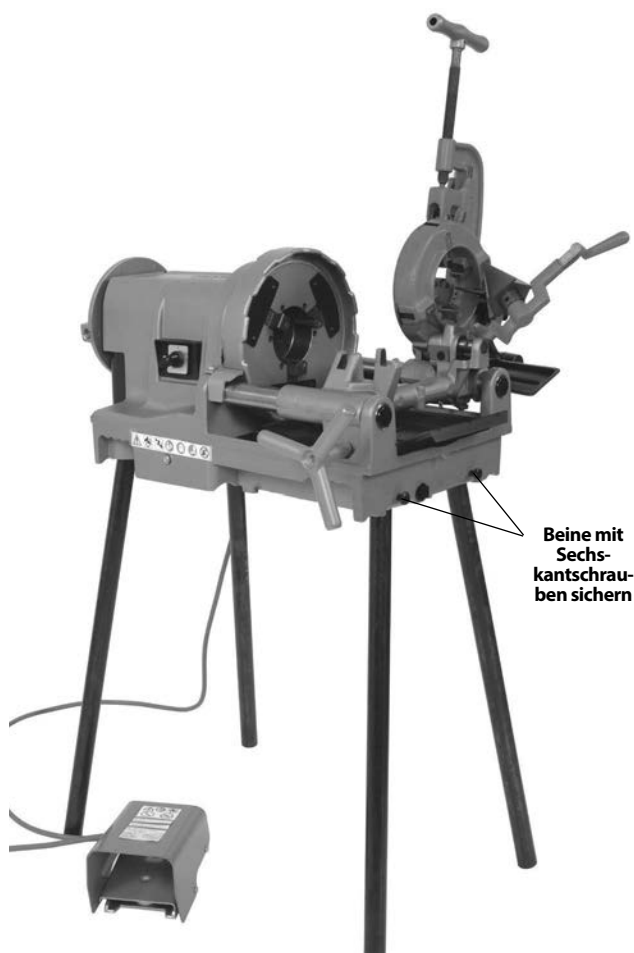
Gewindeschneidmaschine auf Rohrstücke montiert
